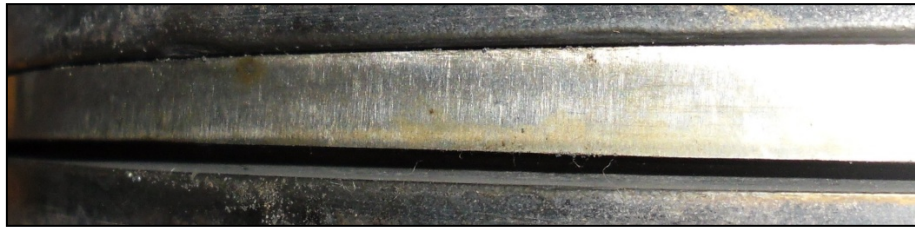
Выработка второй поршневой канавки головки поршня № 6
